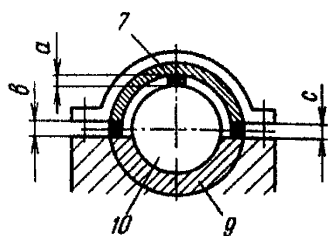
Подшипниковый узел и схема регулировки верхнего зазора подшипников скольжения:
